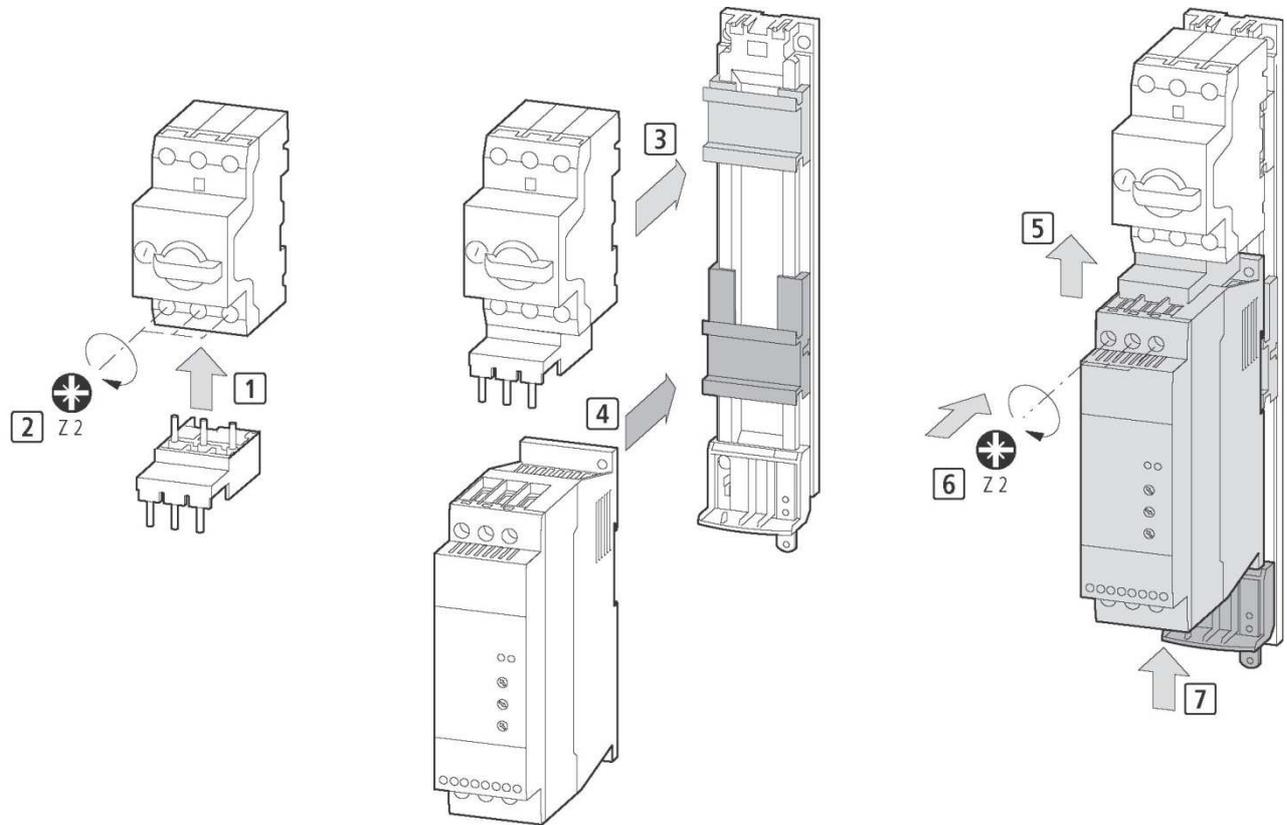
Montaje en carril o en adaptador de embarrado de aparatos de hasta 32 A
